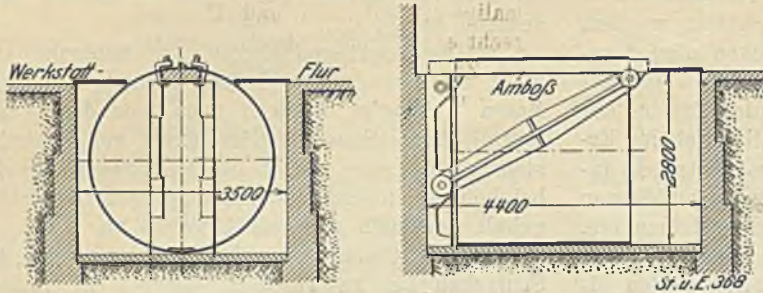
Anordnung beim Schweißen der Längsverbinding.
